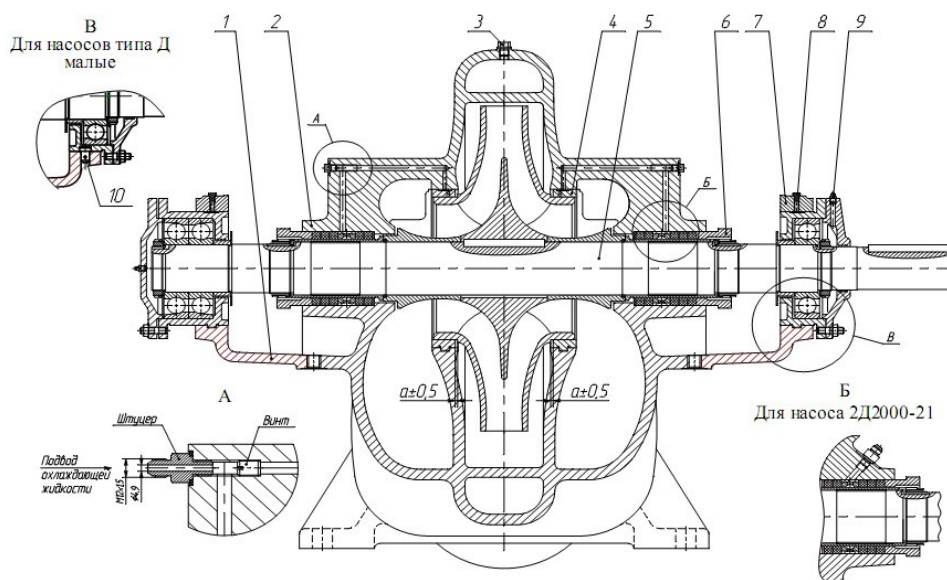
Разрез насоса с двусторонним входом: 1 – нижняя половина корпуса; 2 – крышка корпуса; 3 – пробка отверстия вакуумной системы (выпуска воздуха); 4 – уплотняющие кольца; 5 – ротор (вал насоса с рабочим колесом); 6 – гайка сальника; 8 – отверстие для датчика температуры; 9 – пресс масленка для смазки подшипников; 10 – направляющая втулка.
